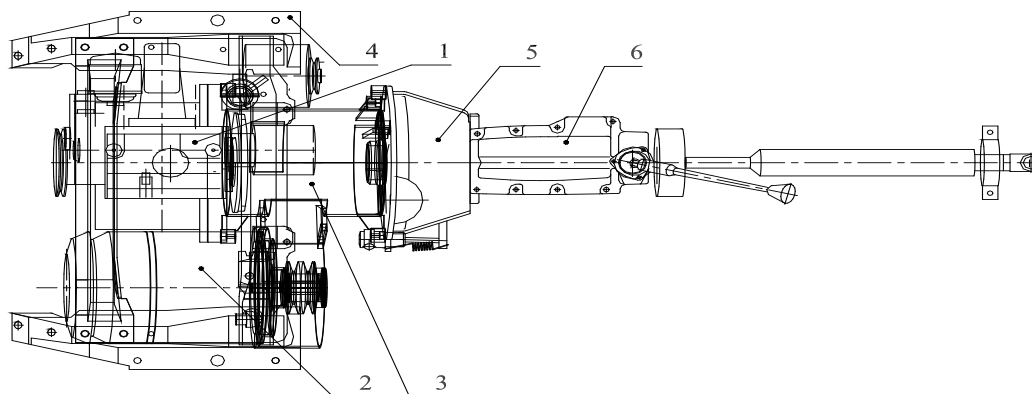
Конструкция КЭСУ (1 – ДВС ВАЗ-1111, 2 – ЭД (генератор), 3 – редуктор, 4 – рама энергетической установки, 5 – сцепление, 6 – коробка передач)
